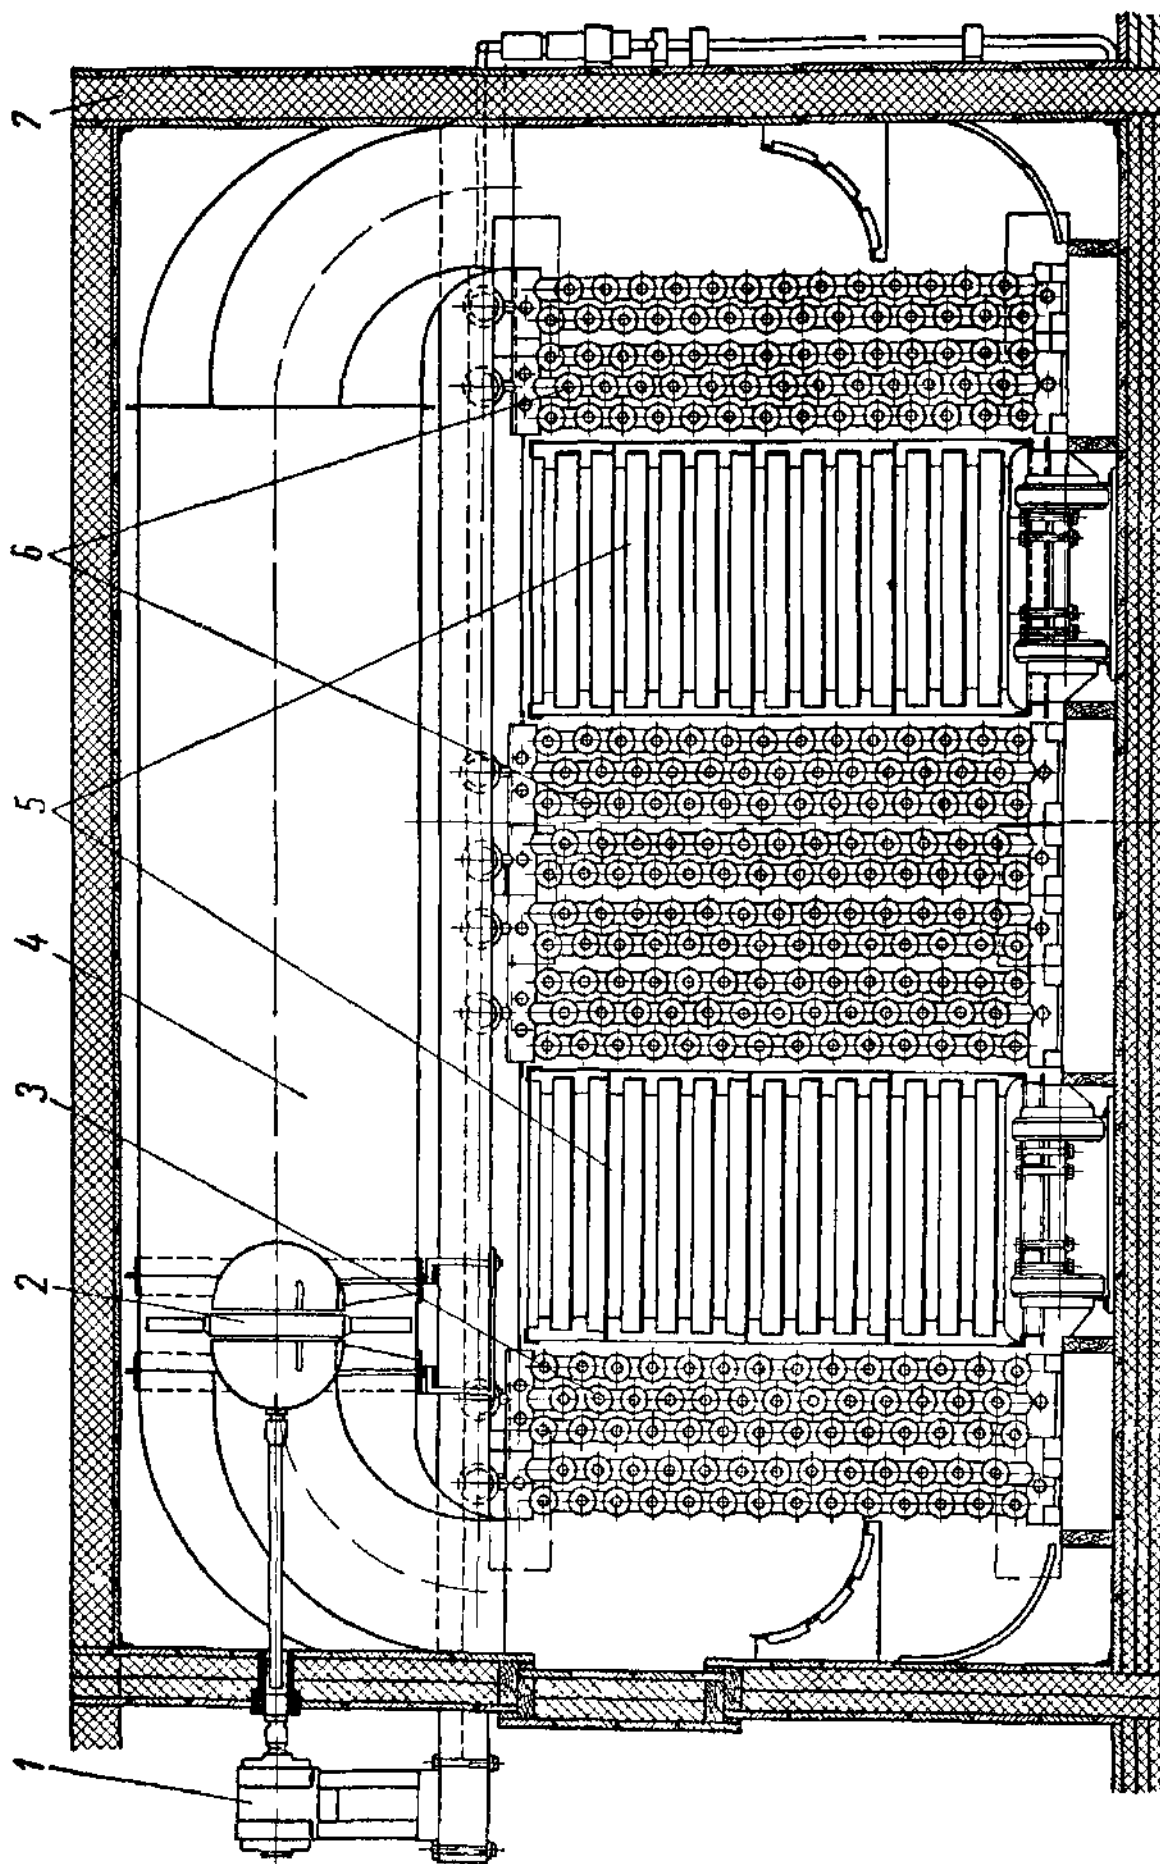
Скороморозильный аппарат с интенсивным движением воздуха
